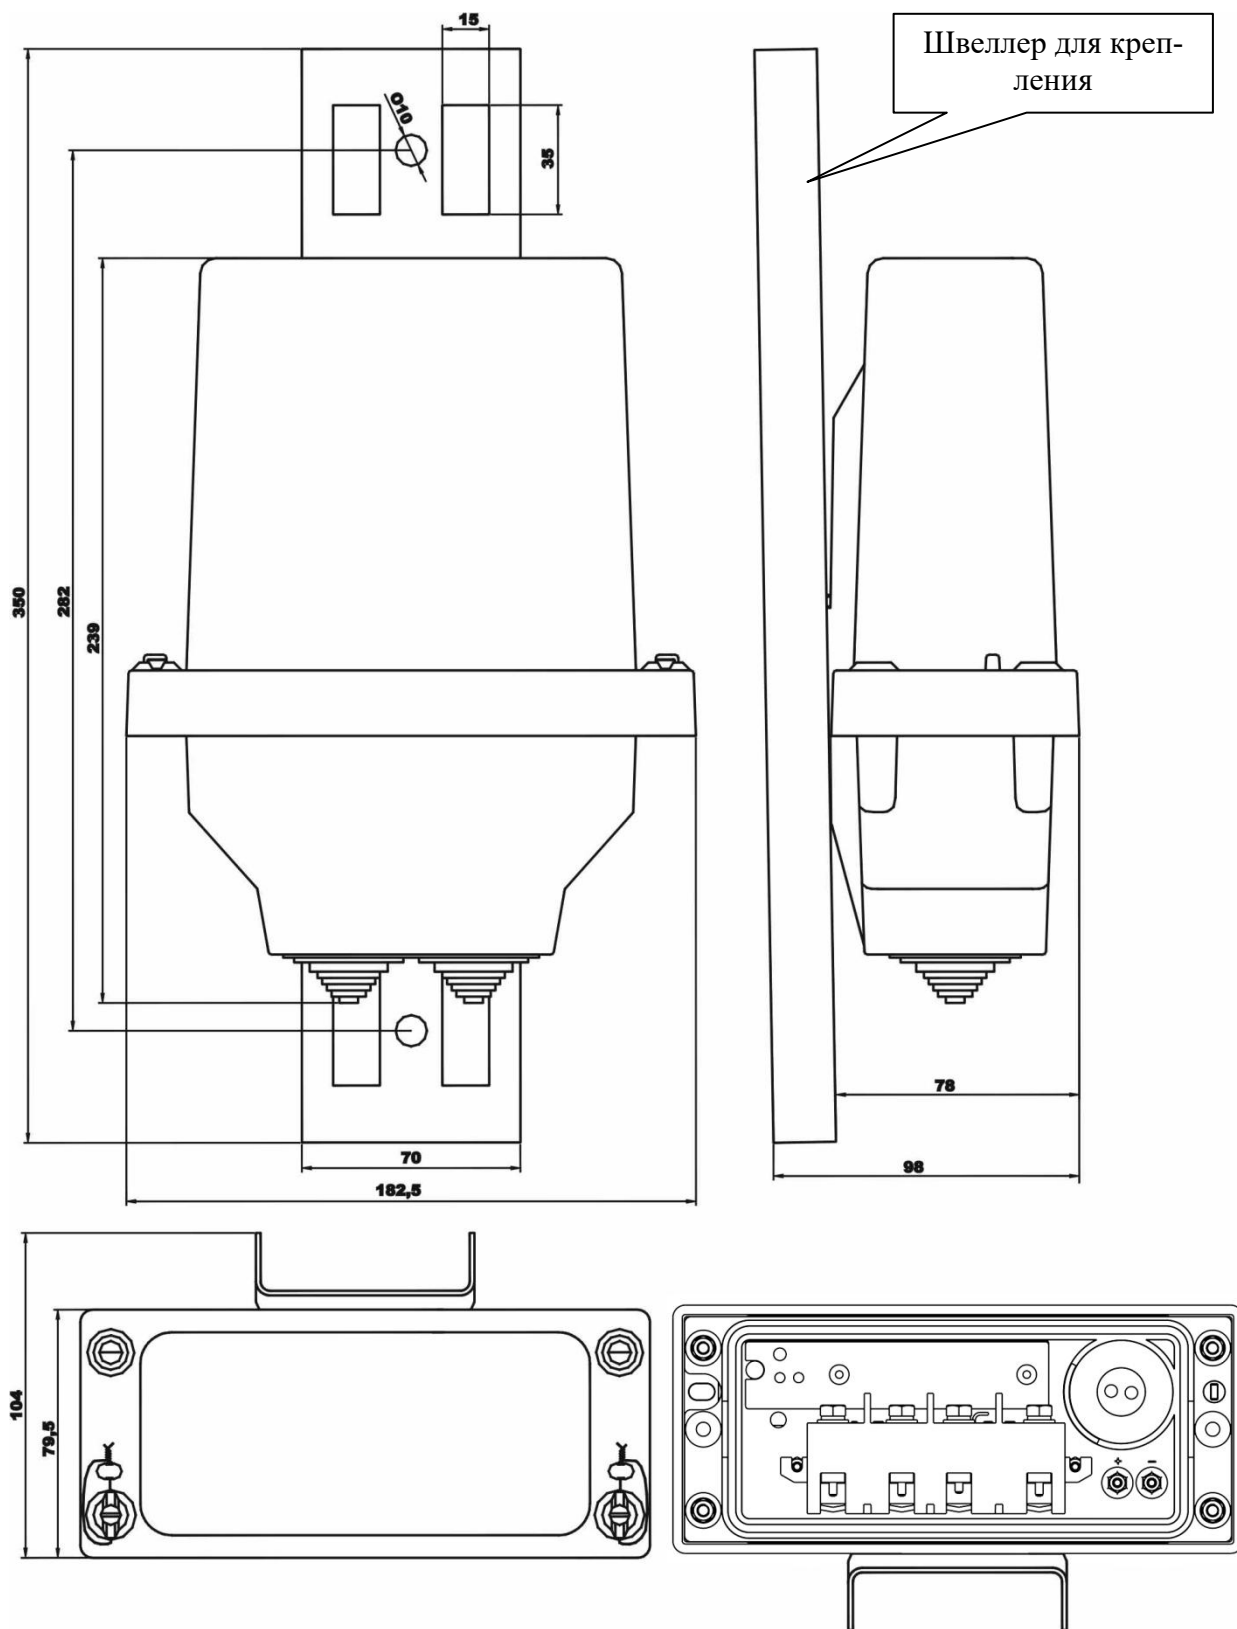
Габаритный чертеж и установочные размеры счётчиков наружной установки СЭБ-1ТМ.04Т.40 – СЭБ-1ТМ.04Т.47
